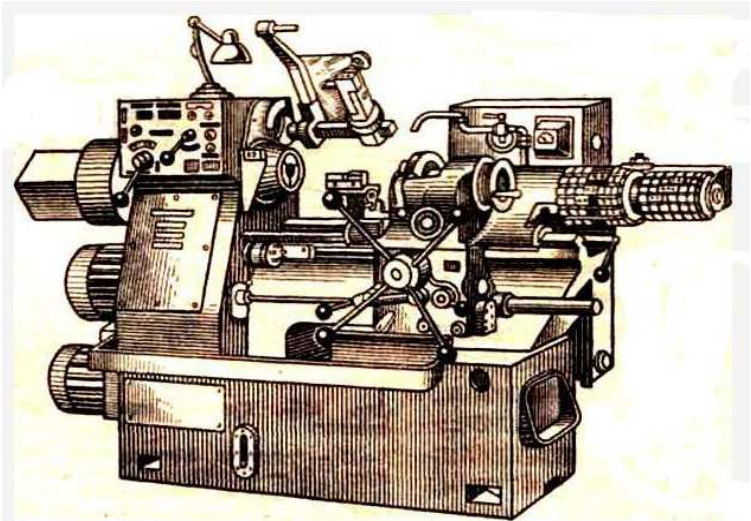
Загальний вигляд токарно-револьверного верстата 1341
